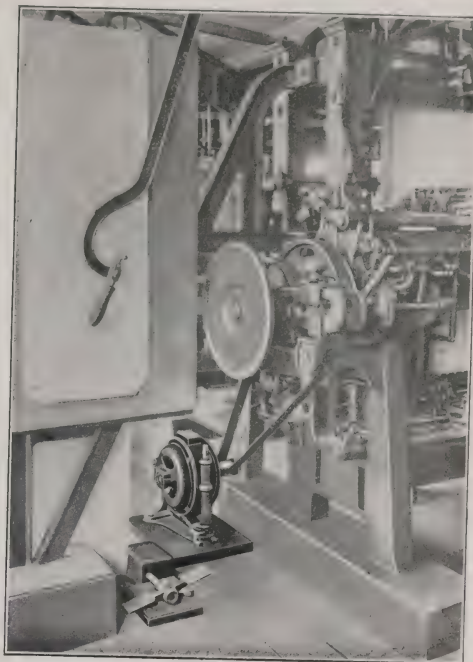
Pantograph-Stickmaschine mit Kurzschlußankermotor.
